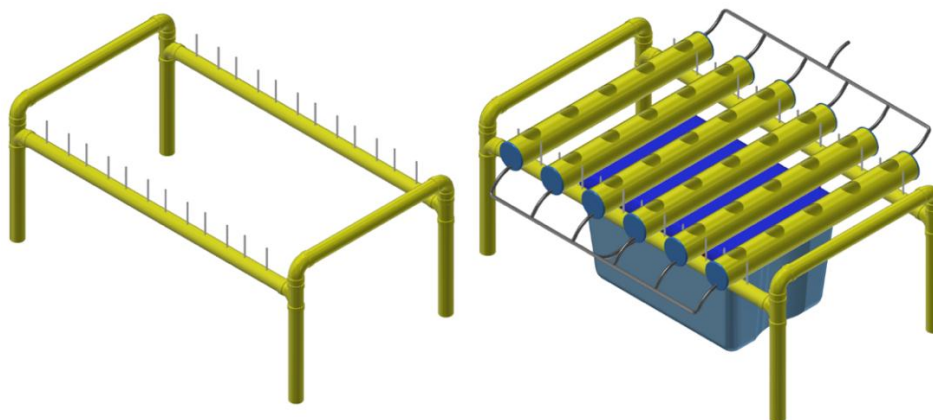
Planos en 3D del sistema de Inundación y drenaje.
